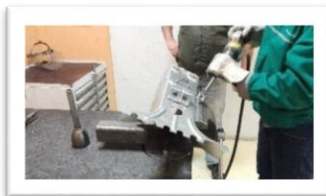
Ponto de Soldadura após Tear Down, Partial Button Pull Failure
